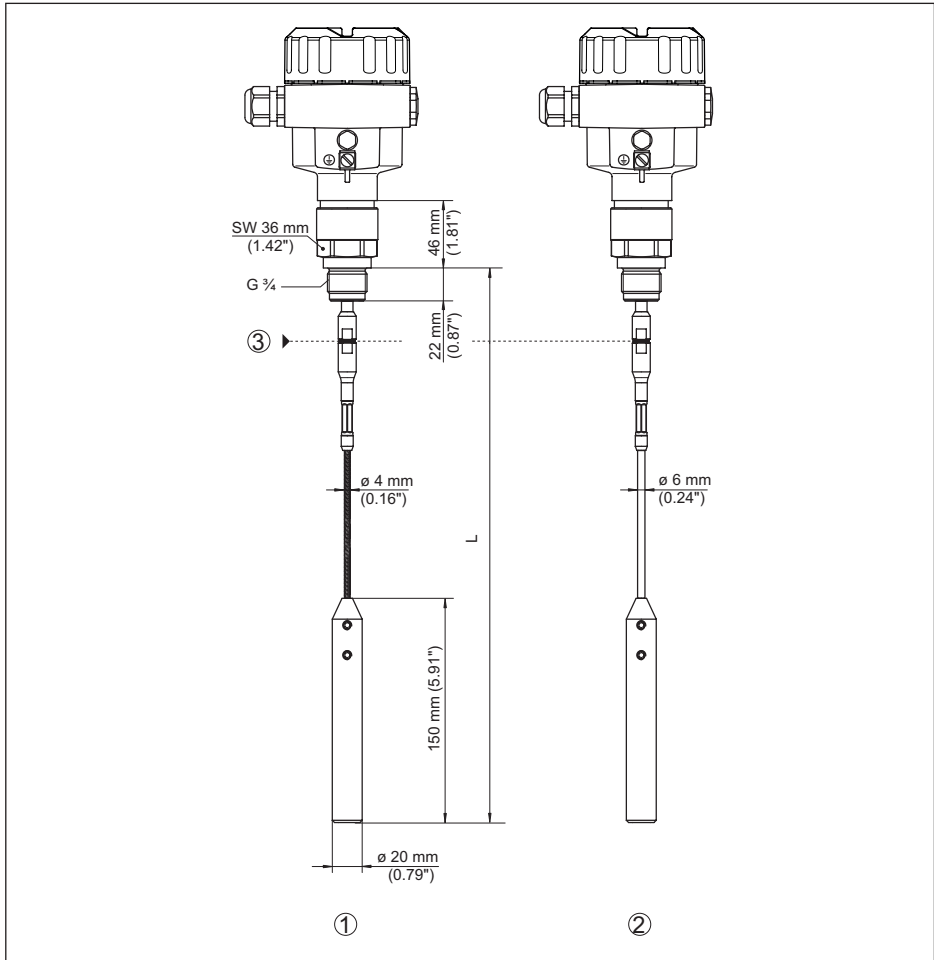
NivoGuide 3100, Seil ø 4 mm (0.157 in), ø 6 mm (0.236 in) Gewindeausführung mit Straffgewicht (alle Straffgewichte mit Gewinde M12 für Ringschraube)
